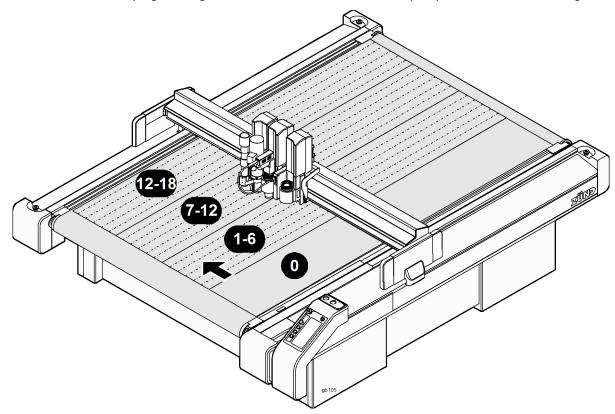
Zone di aspirazione a vuoto (es. L-2500)
